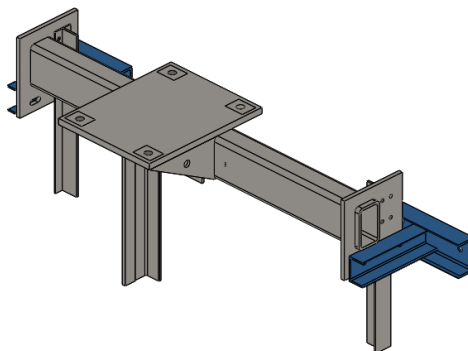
Suporte ancorado nas guias e fixações laterais de parede
